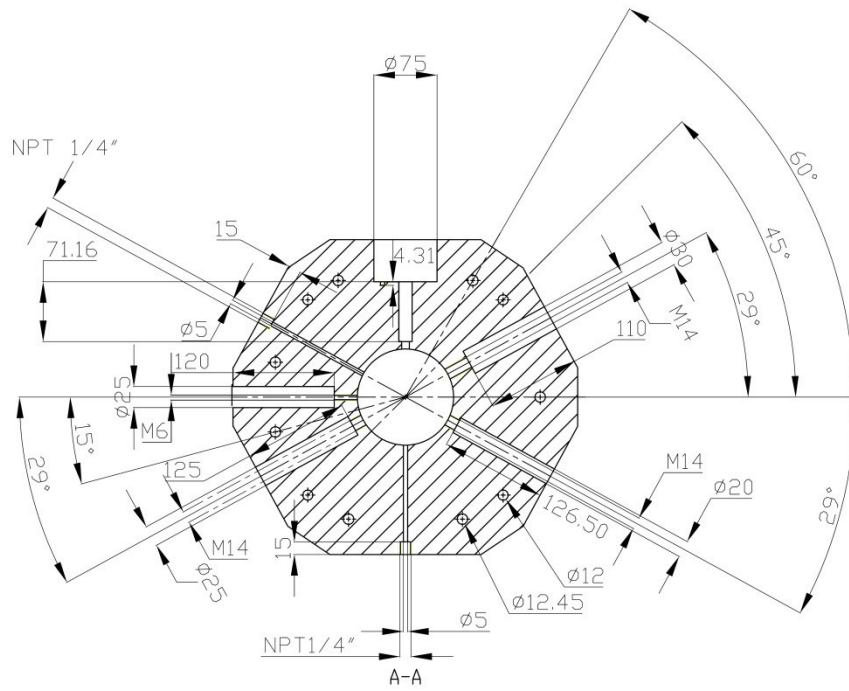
Sección a ½ del alzado del diseño de la bomba de combustión cilíndrica
